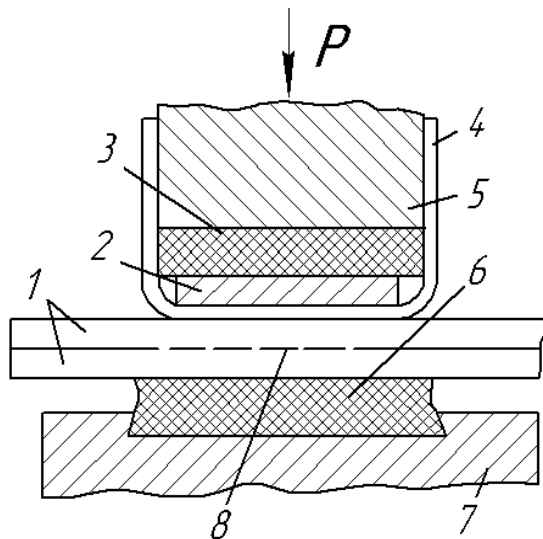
Термоімпульсне зварювання: 1 – зварювані плівки; 2 – нагрівальний інструмент; 3 – тепло електроізоляційна прокладка; 4 – антиадгезійна прокладка; 5 – рухома частина зварювального пристрою; 6 – антиадгезійна підкладка; 7 – нерухома частина зварювального пристрою; 8 – зварний шов.
